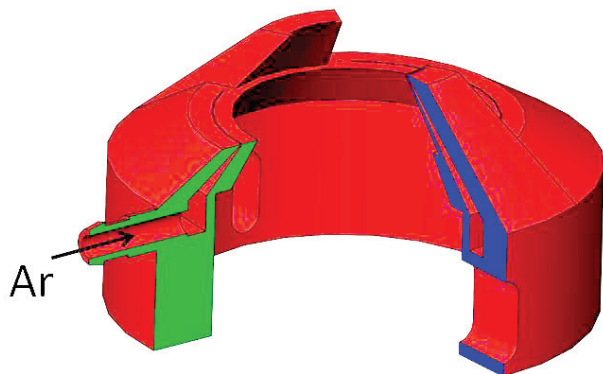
Приспособление для подачи защитного газа в зону сварки
